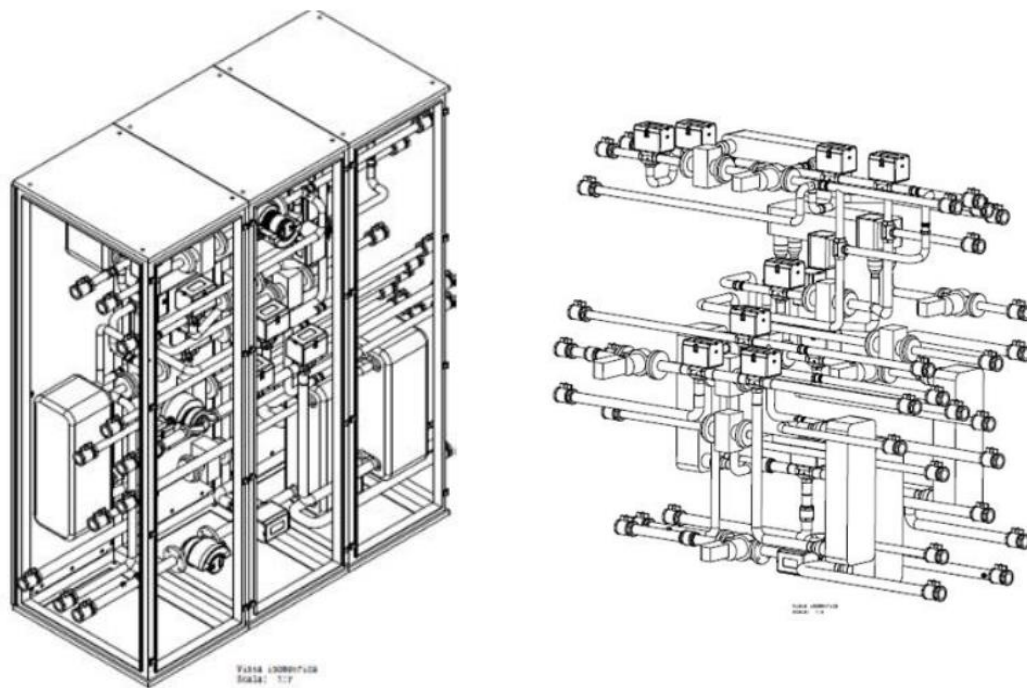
Energy Box vista 3D, Impianto idraulico vista 3D
